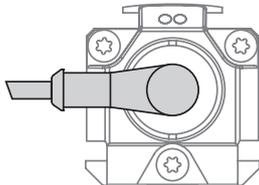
Steckverbinder BKS-S116-PU- _ _ , Abgang
